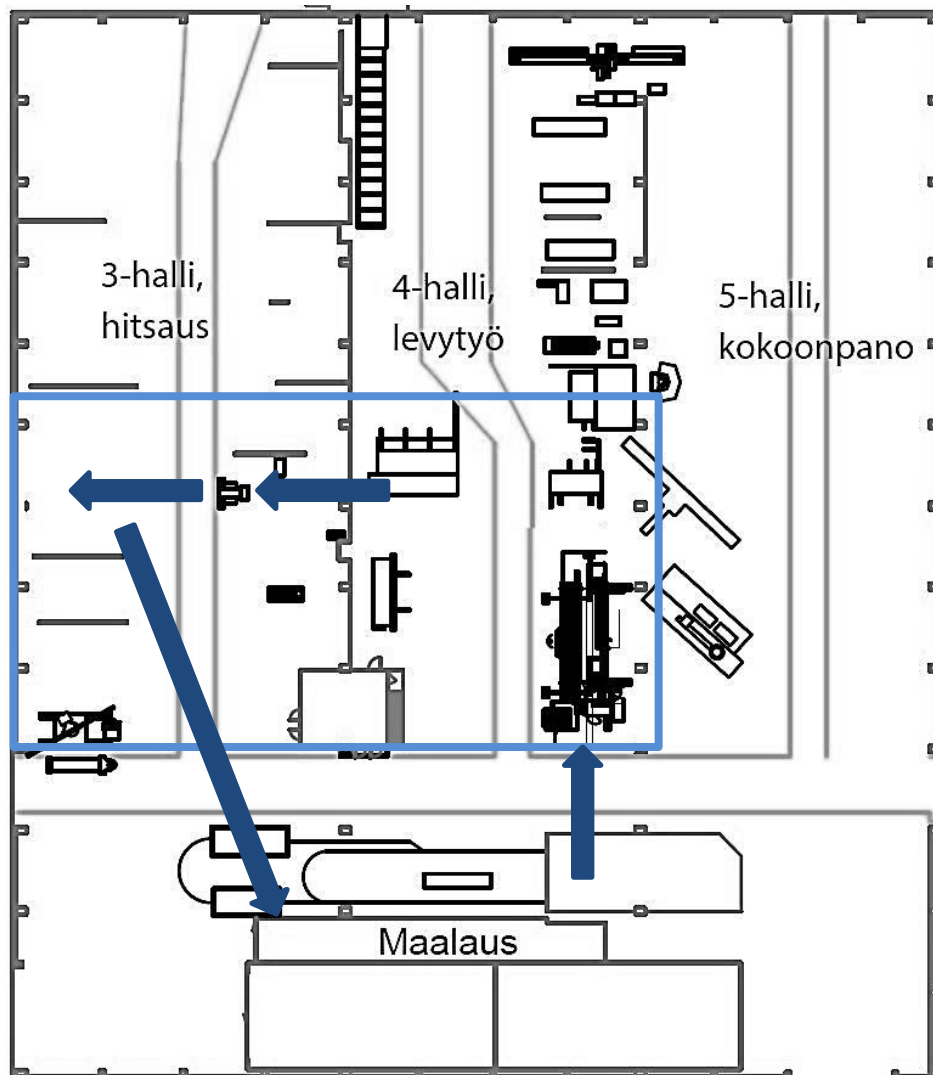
Koneistussolun layout ja osan B työnkulku solussa
